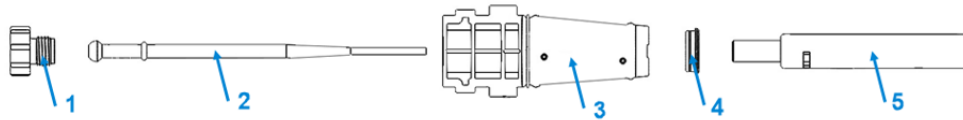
Pièces illustrées de la torche entièrement amovible Agilent
